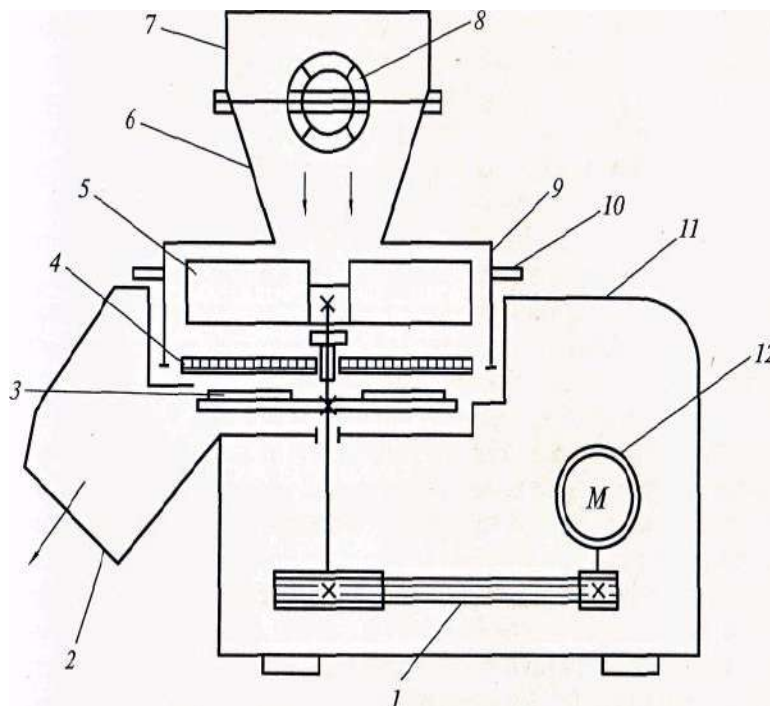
Лопатева протиральна машина: 1 – клинопасова передача; 2 – розвантажувальний лоток; 3 – скидач; 4 – протиральний диск (сито); 5 – лопатевий ротор; 6 – конічна чаша; 7 – обичайка; 8 – запобіжник; 9 – робоча камера; 10 – штифт; 11 – корпус; 12 – електродвигун
